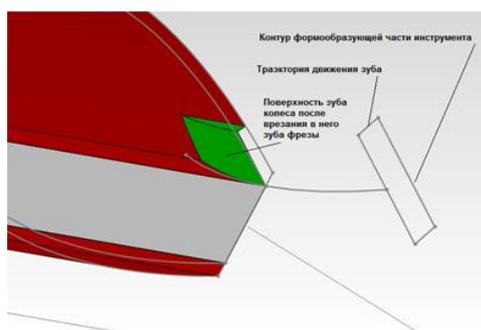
Формирование шероховатости поверхности зубьев колеса после врезания в него зуба фрезы
